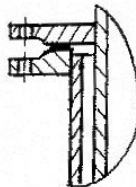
Вариант крепления съемной рубашки к корпусу реактора
